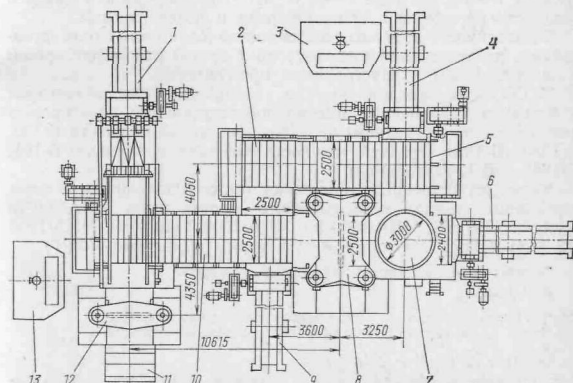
Агрегат для разделки крупных чугуных изложниц и изделий
